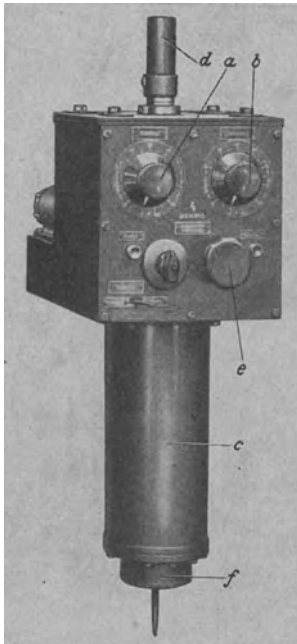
Kohleschweißkopf einer selbsttätigen Schweißeinrichtung.
